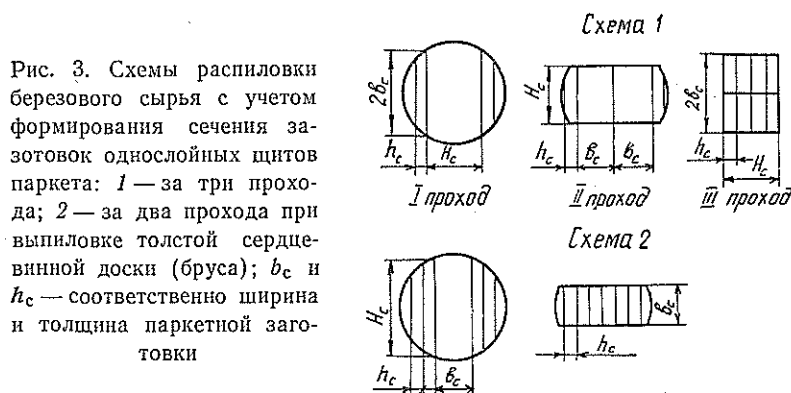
Схемы распиловки березового сырья с учетом формирования сечения заготовок однослойных щитов паркета: 1 — за три прохода; 2 — за два прохода при выпиловке толстой сердцевинной доски (бруса); b_c и h_c — соответственно ширина и толщина паркетной заготовки
